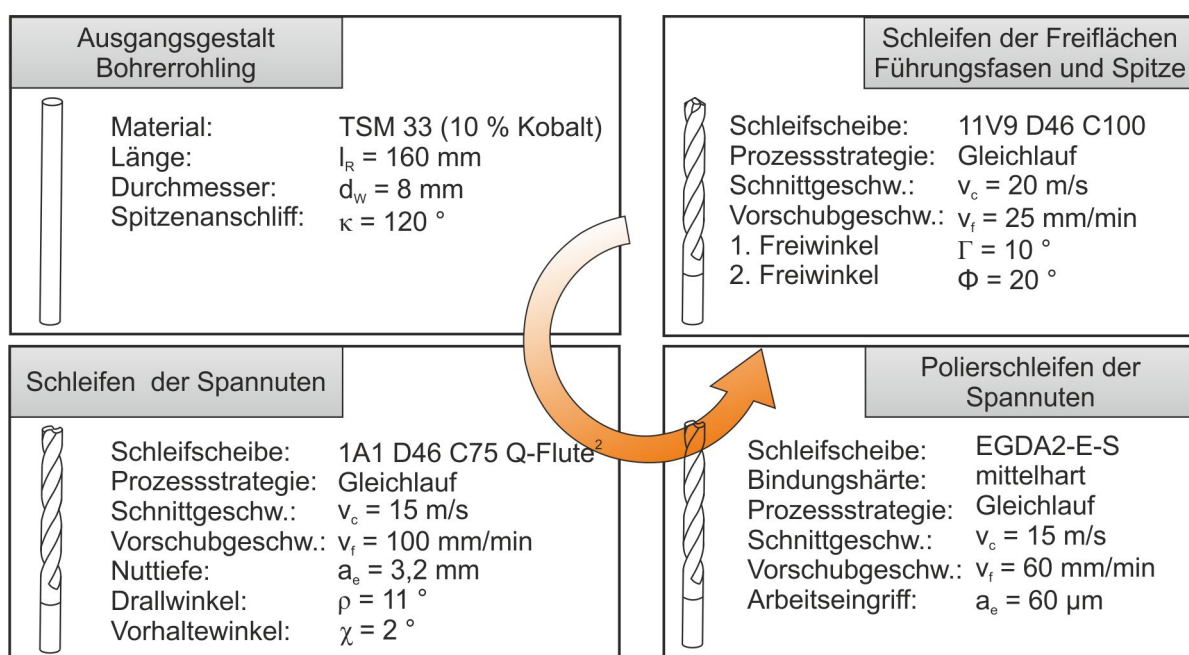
Schleiftechnische Herstellung von VHM-Bohrwerkzeugen
